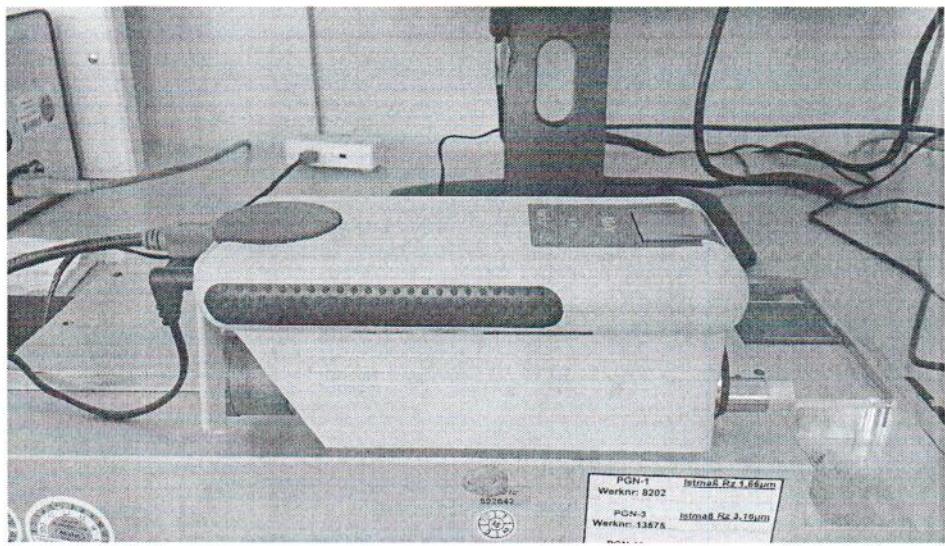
Внешний вид приборов для измерения шероховатости поверхности MarSurf XR1 в составе с SD 26
